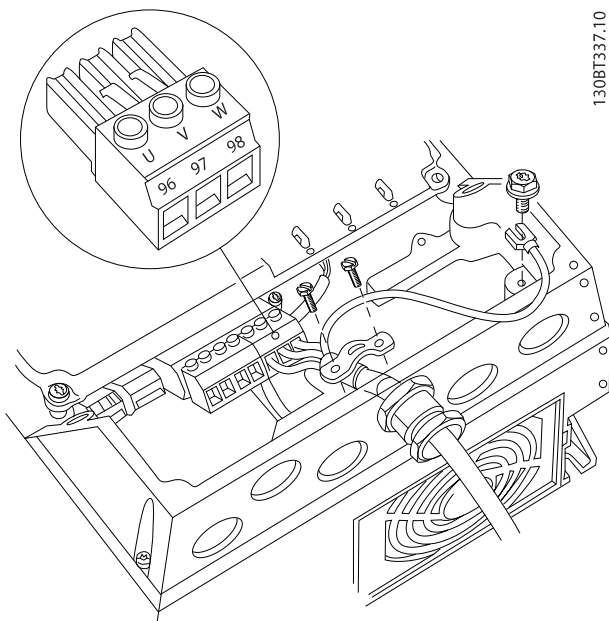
Подключение двигателя, корпуса A4 и A5
